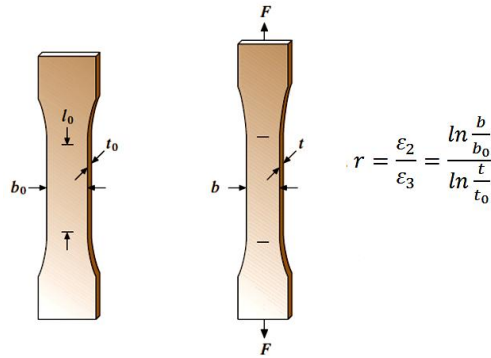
Dimensiones inicial y final de la probeta al aplicar una carga F .
